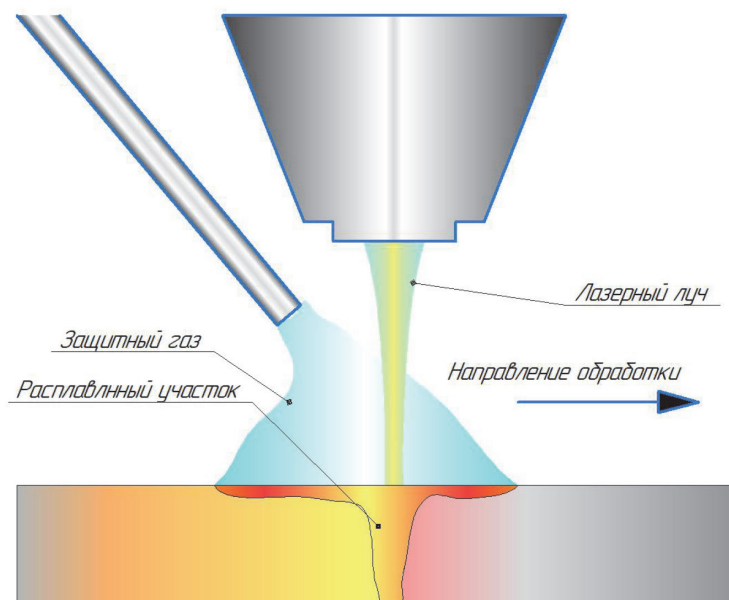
Схема лазерно-дуговой сварки
